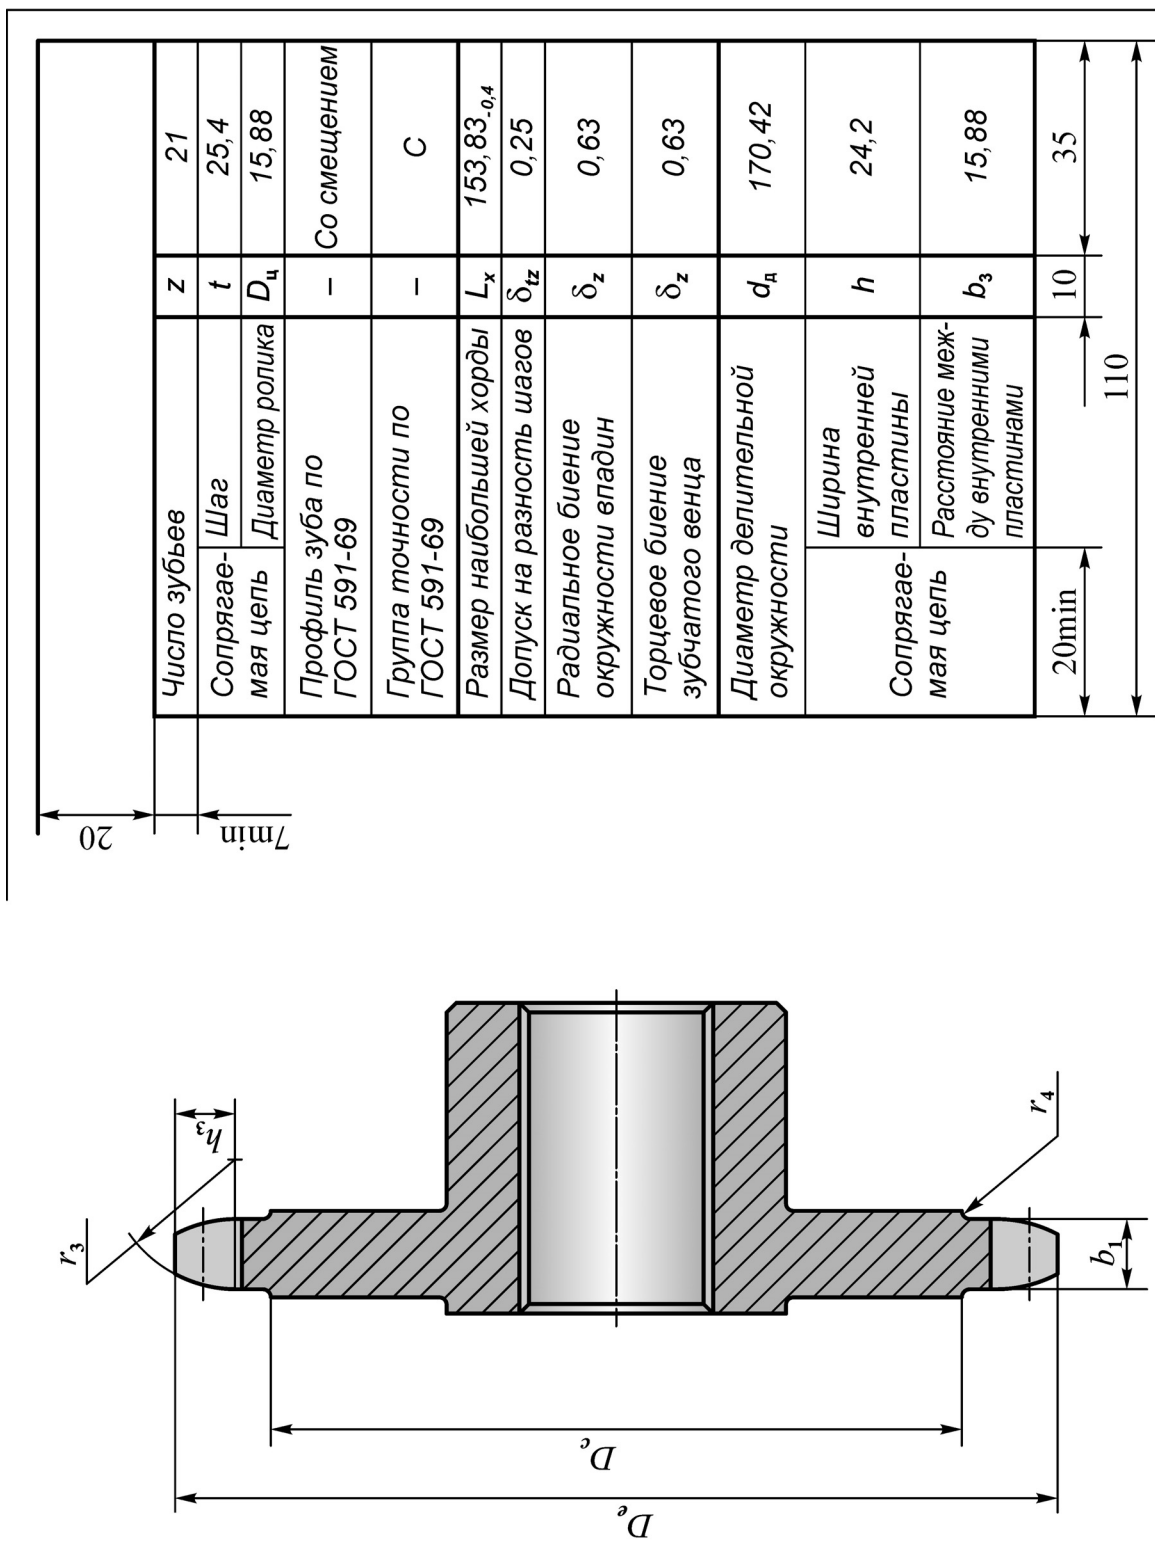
Пример указания параметров зубчатого венца звездочки для приводной роликовой цепи
